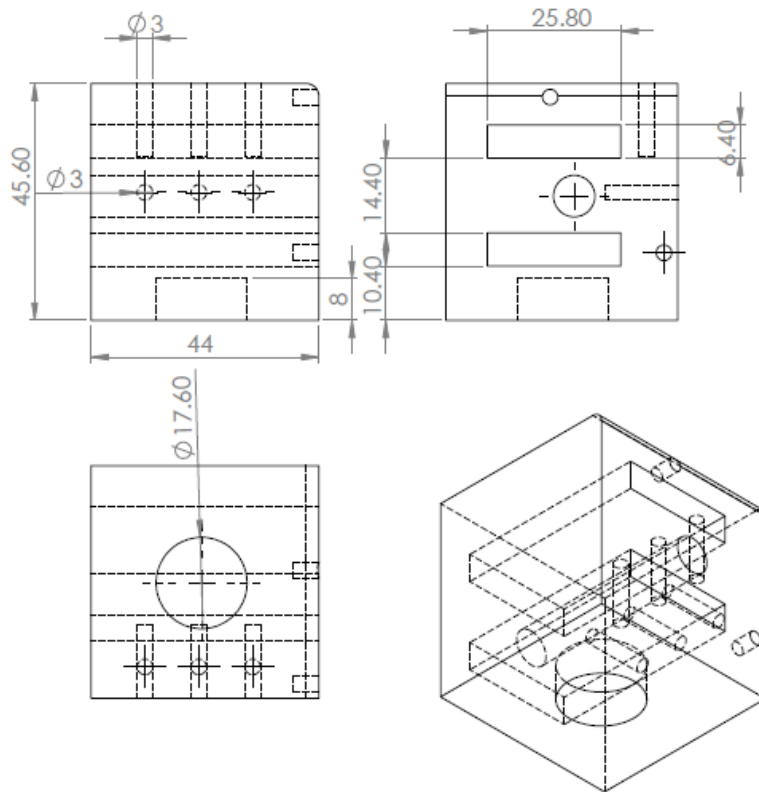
Pieza adaptador que brinda la posición necesaria de las poleas así mismo el paso de los cables tensores y protección de la cámara.
